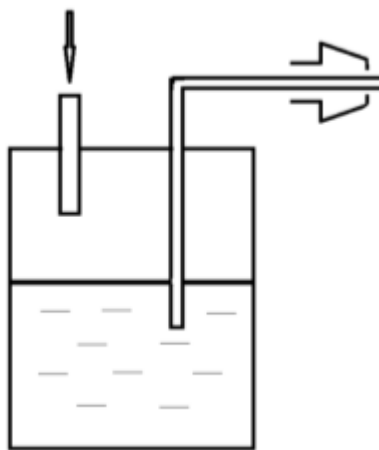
Схема с вытеснением металла из рабочей камеры
